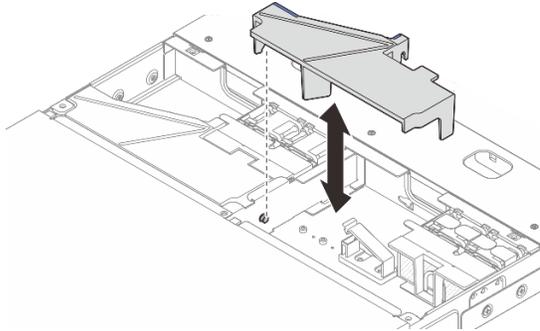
Entfernen der Luftführung für das 1U2N Gehäuse
